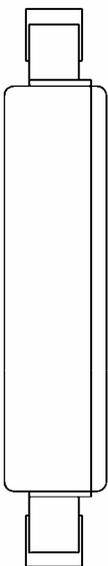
Габаритные чертежи блоков сопряжения МС1 ИТНЯ.468351.122-01,
